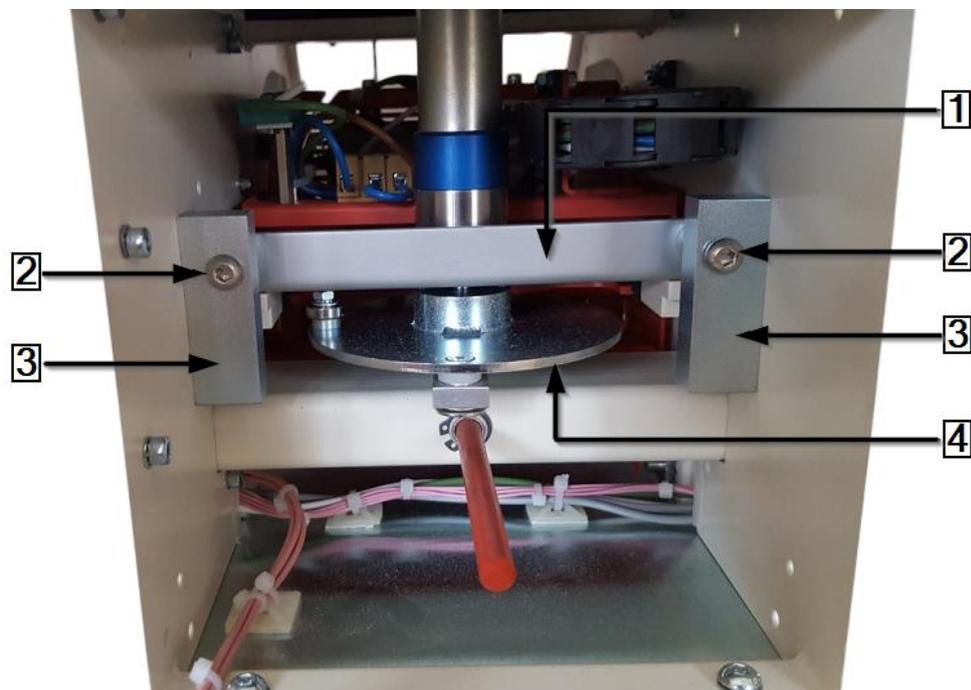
Ajuste de la posición del conjunto del motor (vista posterior)
